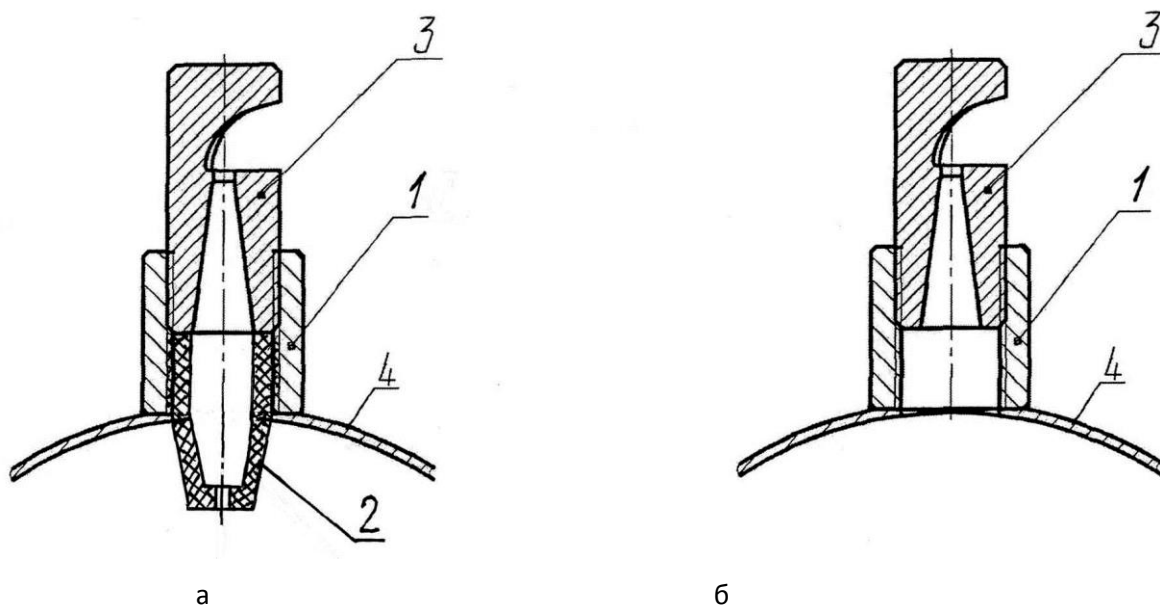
Дождеобразующие устройства для машин типа «Фрегат»:
